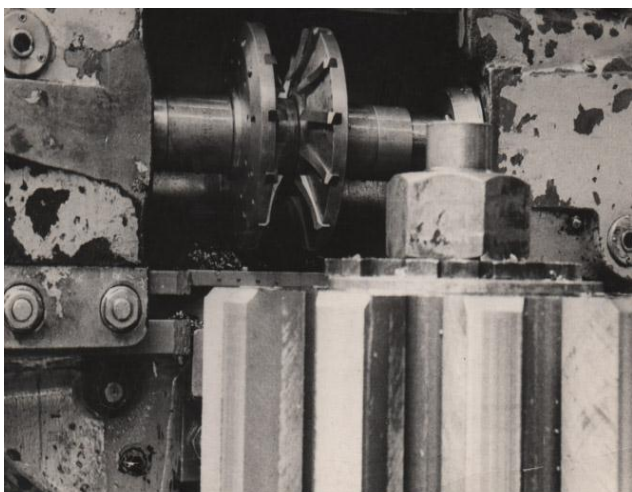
Нарезание шестерни $m=36$ мм $Z=18$ с сопряженным профилем зубьев двумя спаренными дисковыми фрезами
